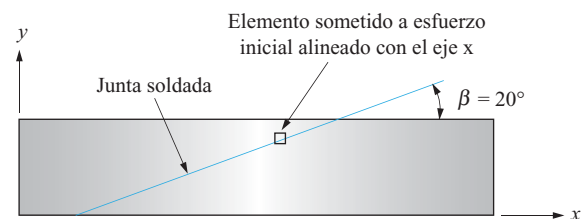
Barra plana soldada a lo largo de una junta inclinada a 20° .
